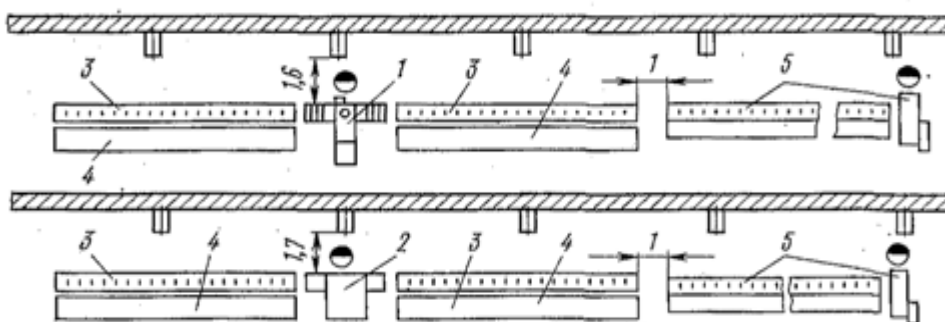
Схеми розташування одностоякових правильних пресів: 1 – гідравлічний прес; 2 – однокривошипний прес; 3 – рольганг; 4 – стіл для заготовок; 5 – суміжне обладнання
